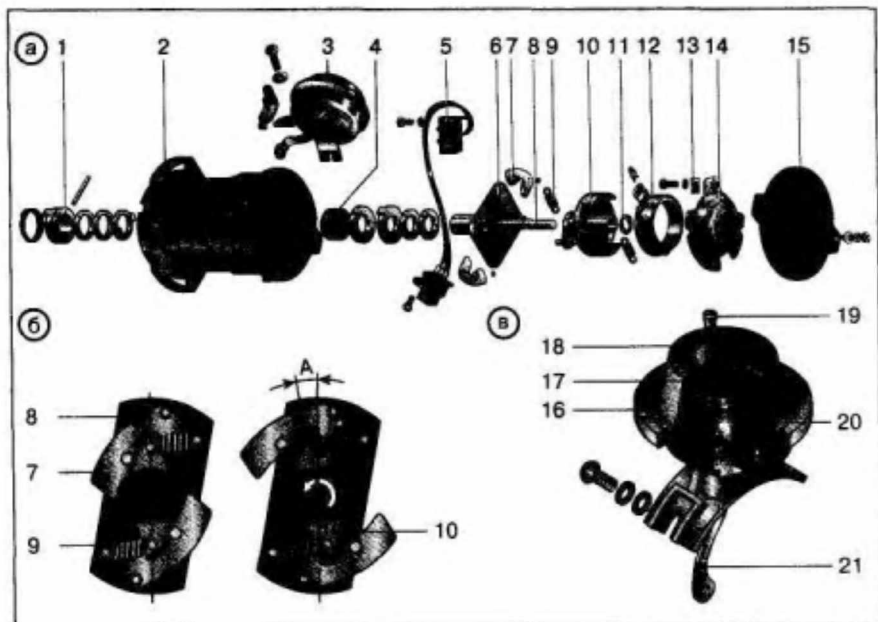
Датчик момента искрообразования: а — устройство; б — центробежный регулятор; в — вакуумный регулятор; 1 — муфта; 2 — корпус датчика; 3 — вакуумный регулятор; 4 — сальник; 5 — датчик импульсов напряжения (датчик Холла); 6 — центробежный регулятор; 7 — грузик; 8 — валик с пластиной грузиков; 9 — пружина; 10 — ведомая пластина центробежного регулятора с экраном; 11 — стопорная шайба; 12 — опорная пластина с подшипником; 13 — стопорная пластина подшипника; 14 — держатель переднего подшипника валика; 15 — крышка; 16, 18 — крышки вакуумного регулятора; 17 — пружина; 19 — штуцер для подвода разрежения; 20 — диафрагма; 21 — тяга вакуумного регулятора
